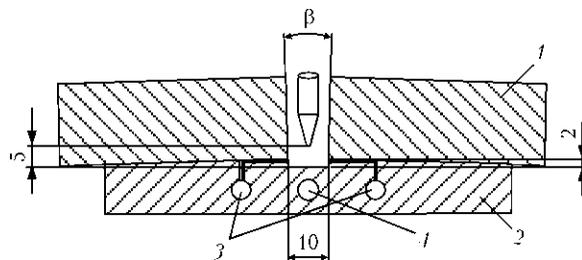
Схема сборки деталей под сварку: 1 — свариваемые плиты; 2 — формирующая подкладка; 3, 4 — соответственно отверстия для подачи защитного газа и протока охлаждающей воды
